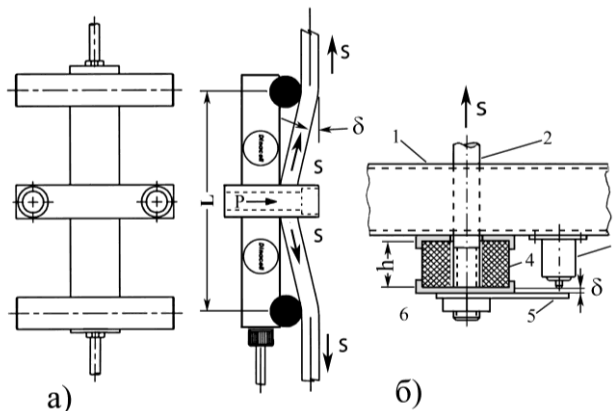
Устройства контроля загрузки кабины путем измерения натяжения канатов подвески кабины:
